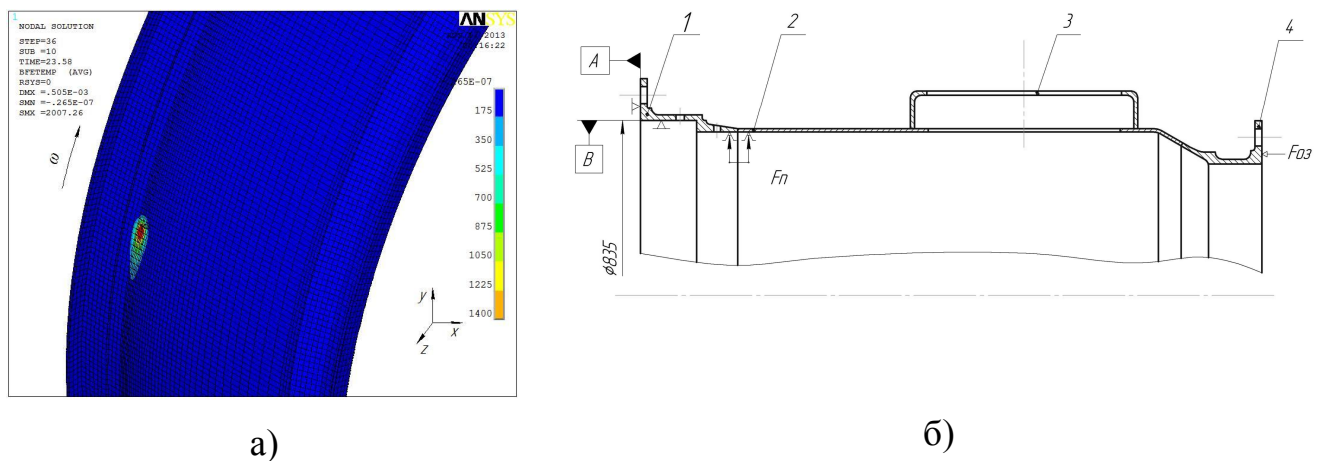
Распределение температурных полей от комбинированного источника нагрева (а) и схема базирования корпуса ТНД в сварочном приспособлении (б)
